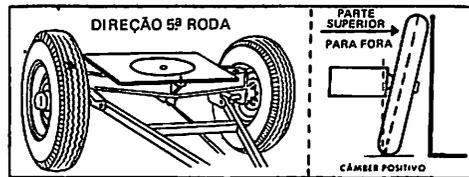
Sistema de direção com quinta roda e cambagem da roda de direção
